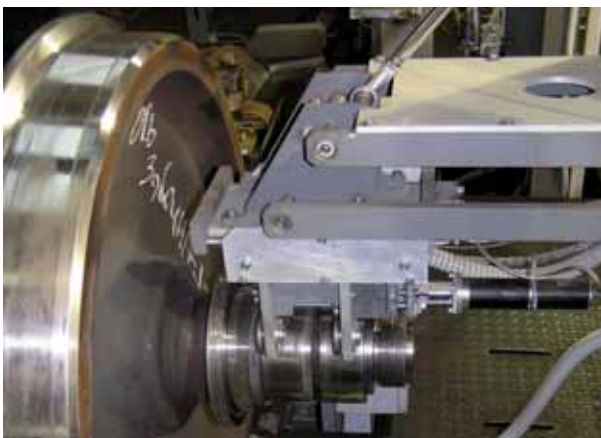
Вихретоковый сканер внутренних колец подшипников буксового узла
